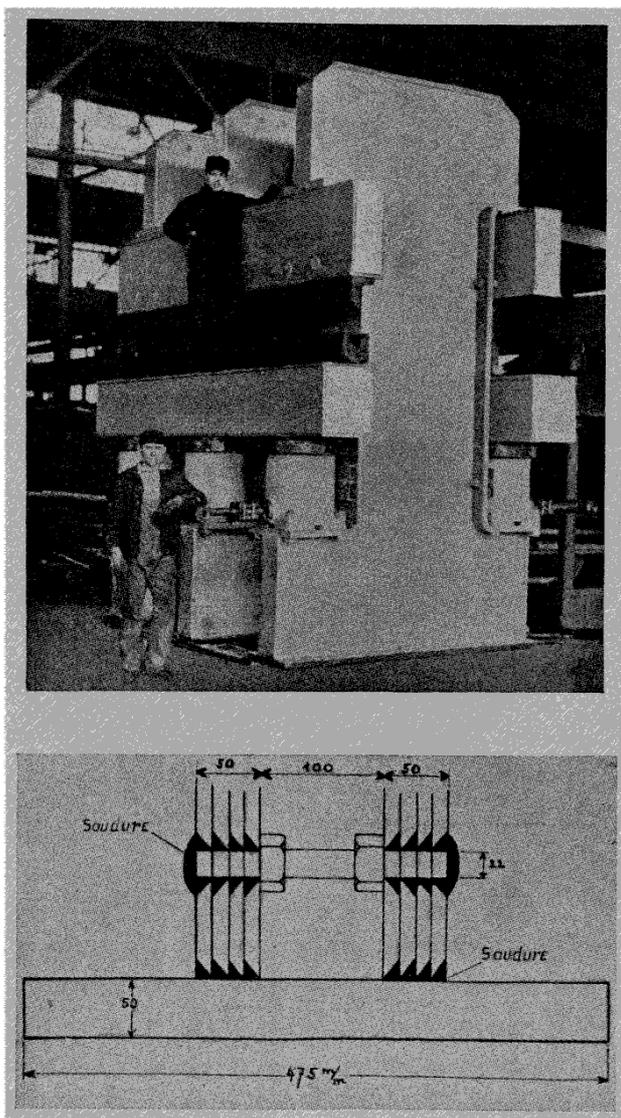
Bâti de presse entièrement soudé et schéma montrant la manière dont les montants sont constitués.
